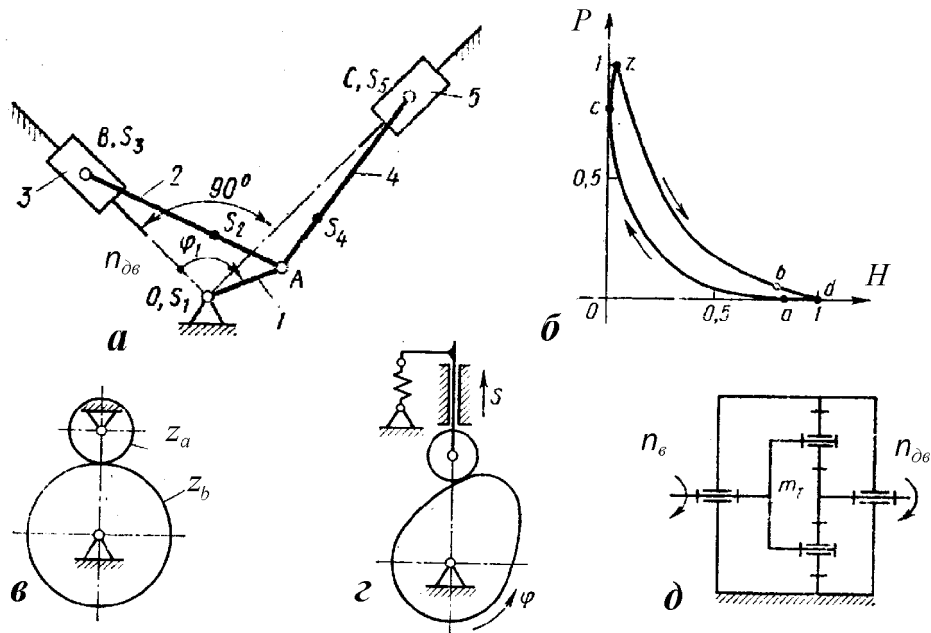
На схеме: а- рычажный механизм двигателя; б- индикаторные диаграммы дизеля; в- стартерная зубчатая передача; г- кулачковый механизм привода масляного насоса; д- привод воздуходувки.
